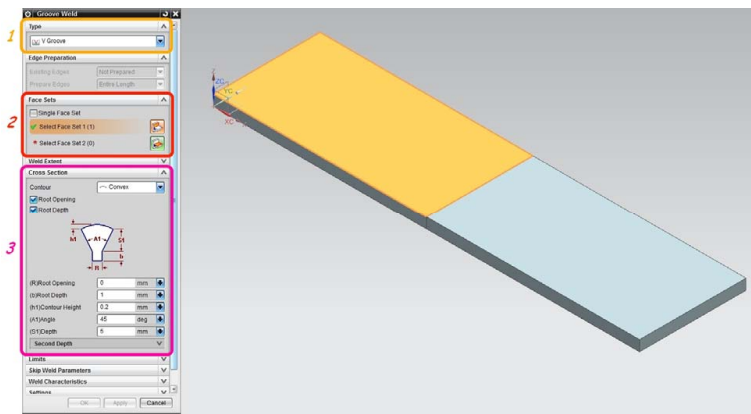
Выбор места сварки и задание параметров сечения шва
